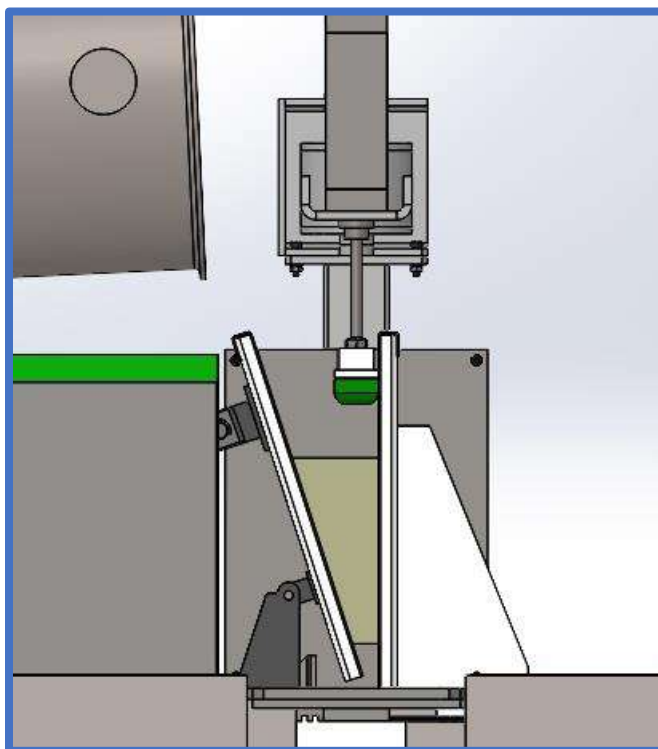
PASO 3 – Posicionado del "Pistón"
